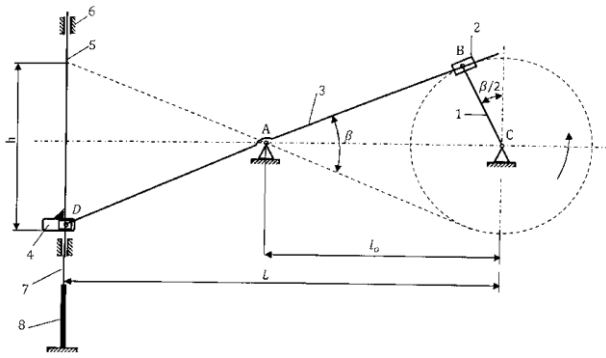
Кинематическая схема кривошипно-кулисного механизма (1- кривошип, 2 – кулисный камень, 3- кулиса, 4 – плавающий ползун, 5 – направляющая) [6]
